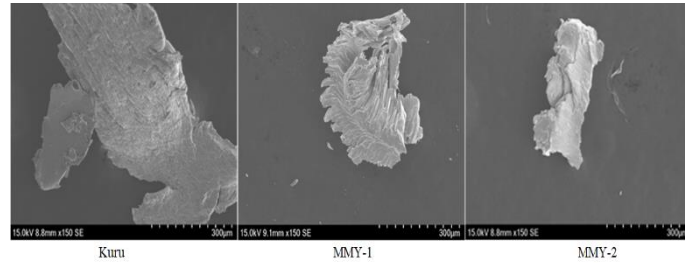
Farklı kesme hızlarında oluşan talaşlar (TiSiN kaplamalı kesici takım, kuru işleme ve geleneksel mikro frezeleme) (Figure 3. Chips formed at different cutting speeds (TiSiN coated cutting tool, dry machining and conventional micro milling))
